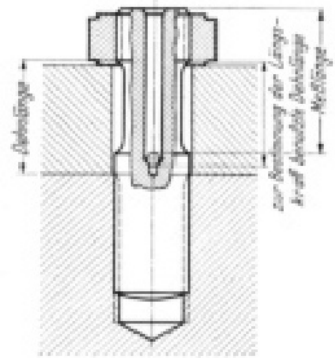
Längsbohrung in Schrauben von großem Durchmesser zum Messen der elastischen Längung.
